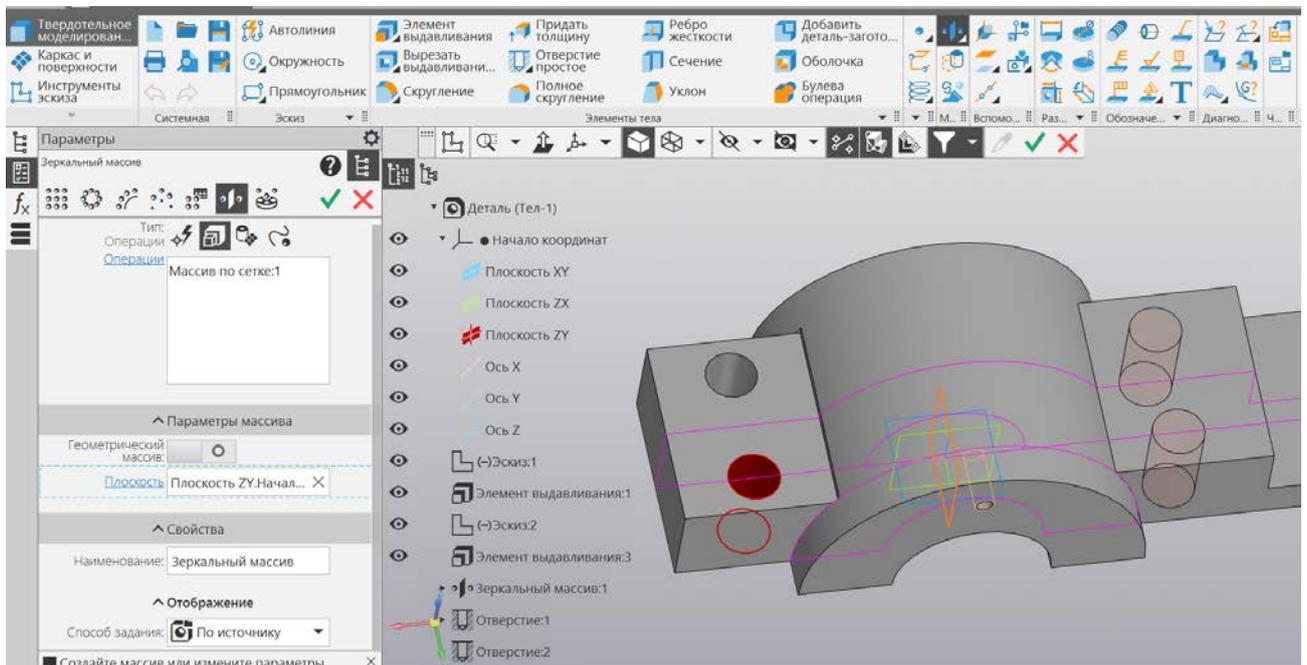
Отражение двух отверстий под шпильки при помощи зеркала
